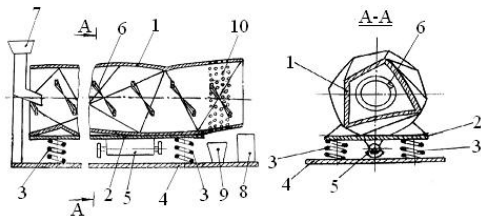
Роторно-винтовой станок с виброконтнером с пружиной растяжения
